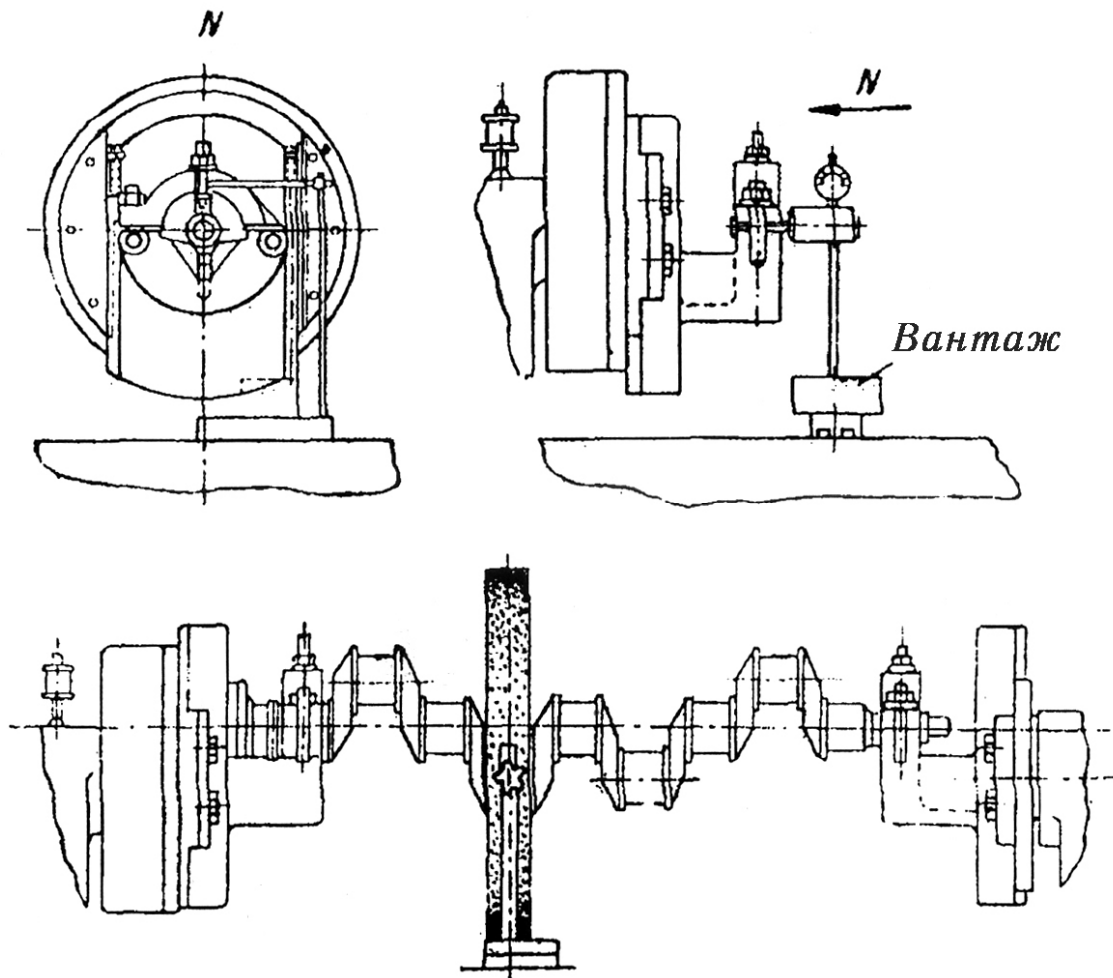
Схема установки вала для шліфування шатунних шийок
